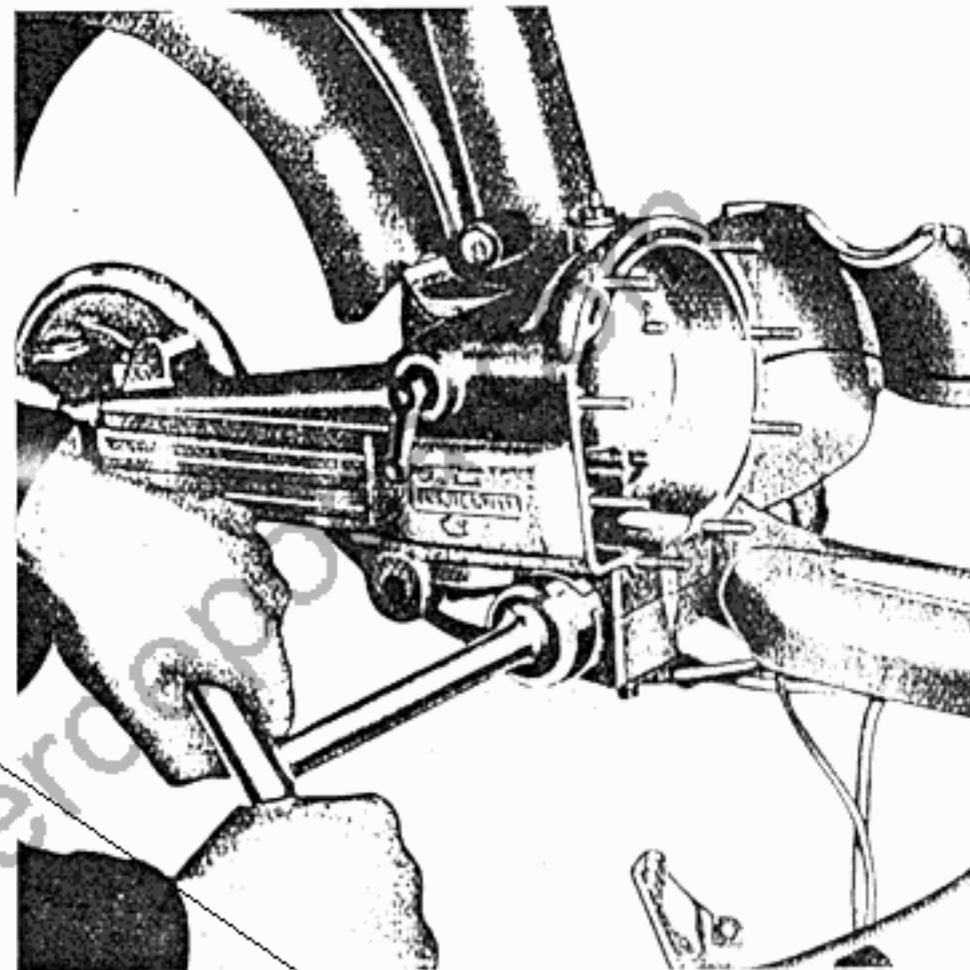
Smontaggio ghiera fissaggio carter trasmissione al cannotto rotazione motore
